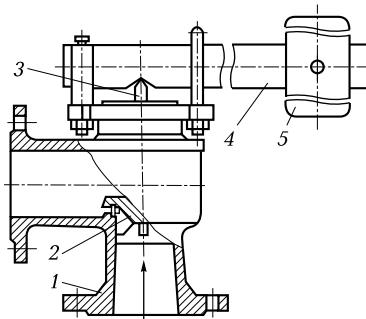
Фланцевый предохранительный рычажно-грузовой клапан:
